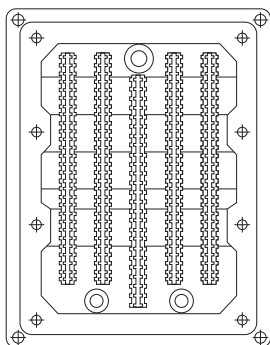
Охладитель под силовой IGBT-модуль с размерами корпуса 170×130 мм, с емкостью для охлаждающей жидкости
